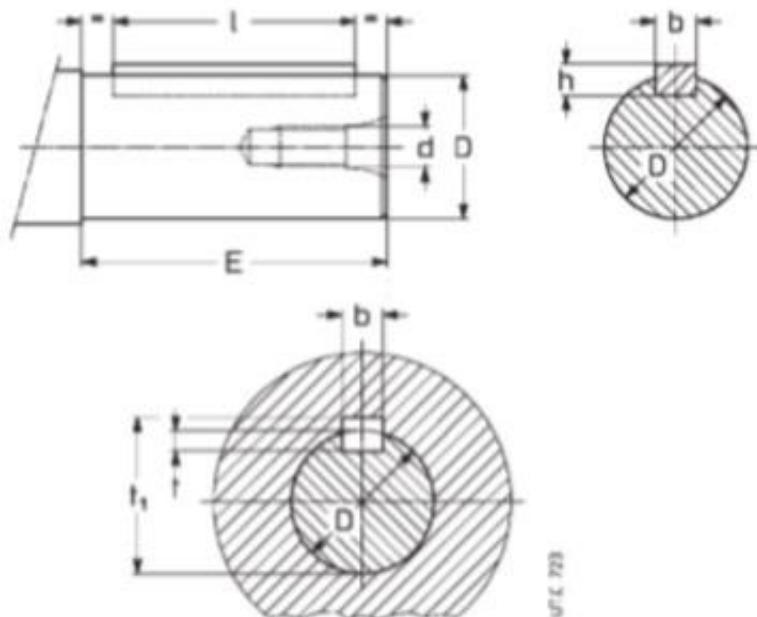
Dimensiones del extremo del árbol de salida del reductor.
